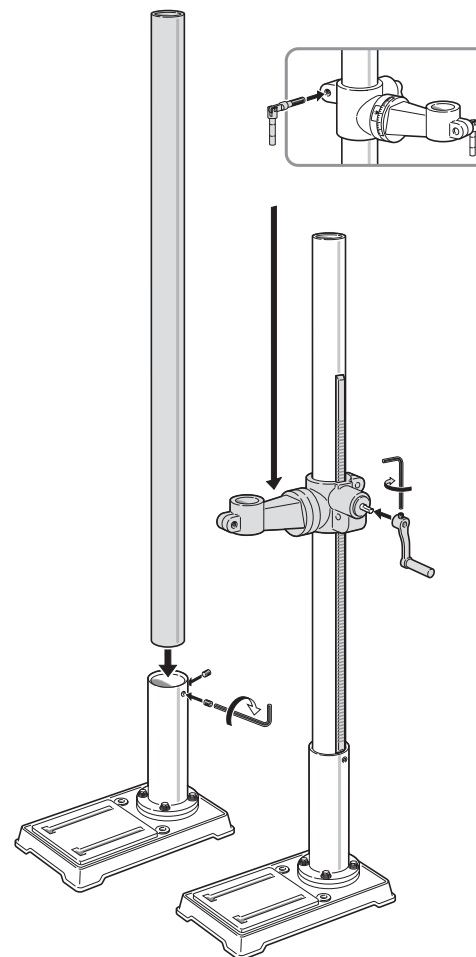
INSTALLATION DU LEVIER DE BLOCAGE ET DE LA MANIVELLE DU PLATEAU
